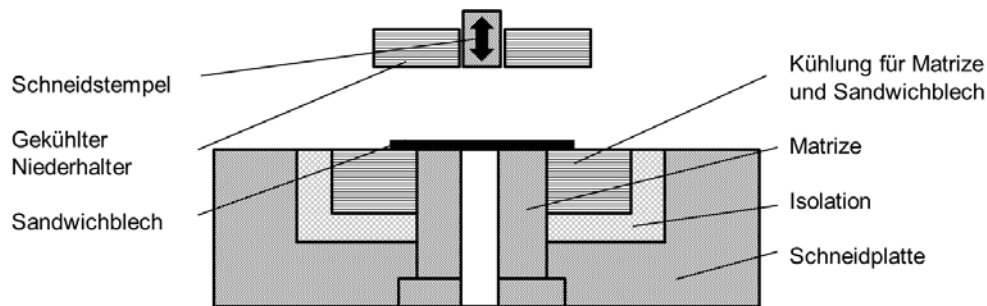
Verfahrensvariante mit gekühlten Werkzeugaktivelementen
